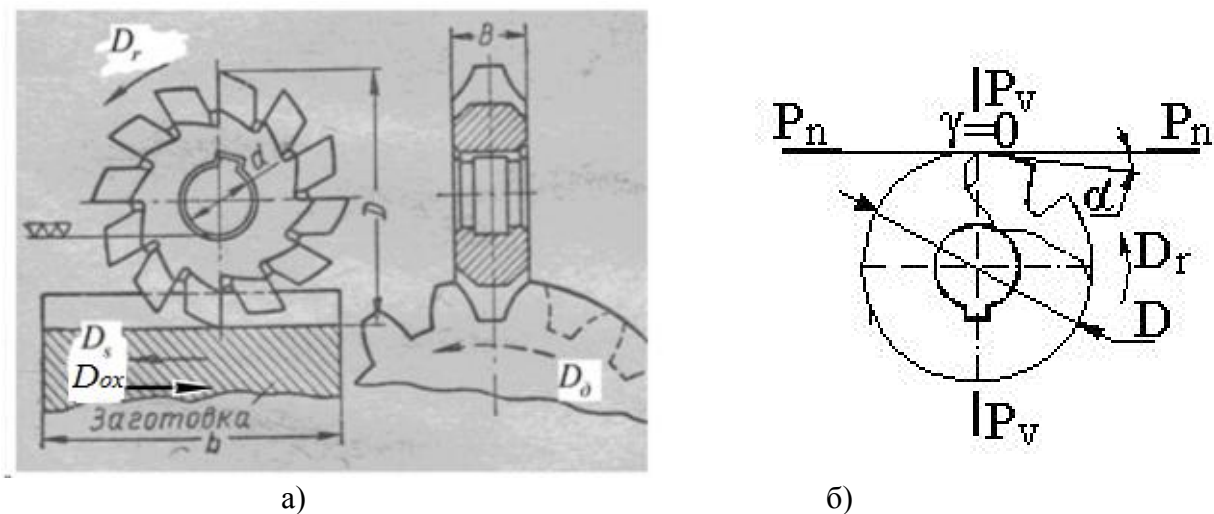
Схема нарезания (а) зубчатых колес и геометрия (б) дисковой модульной фрезы
